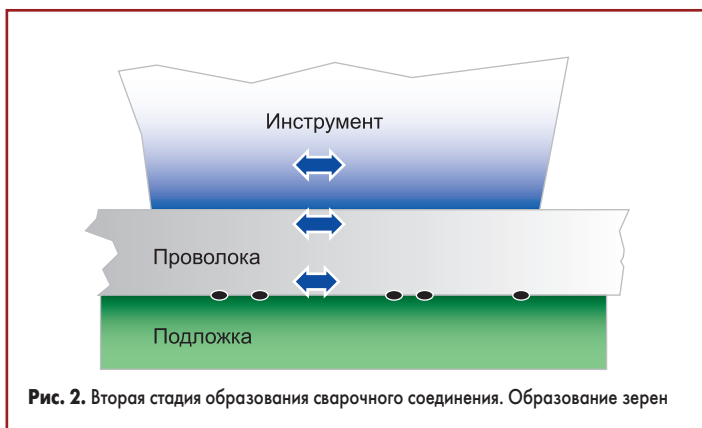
Вторая стадия образования сварочного соединения. Образование зерен
